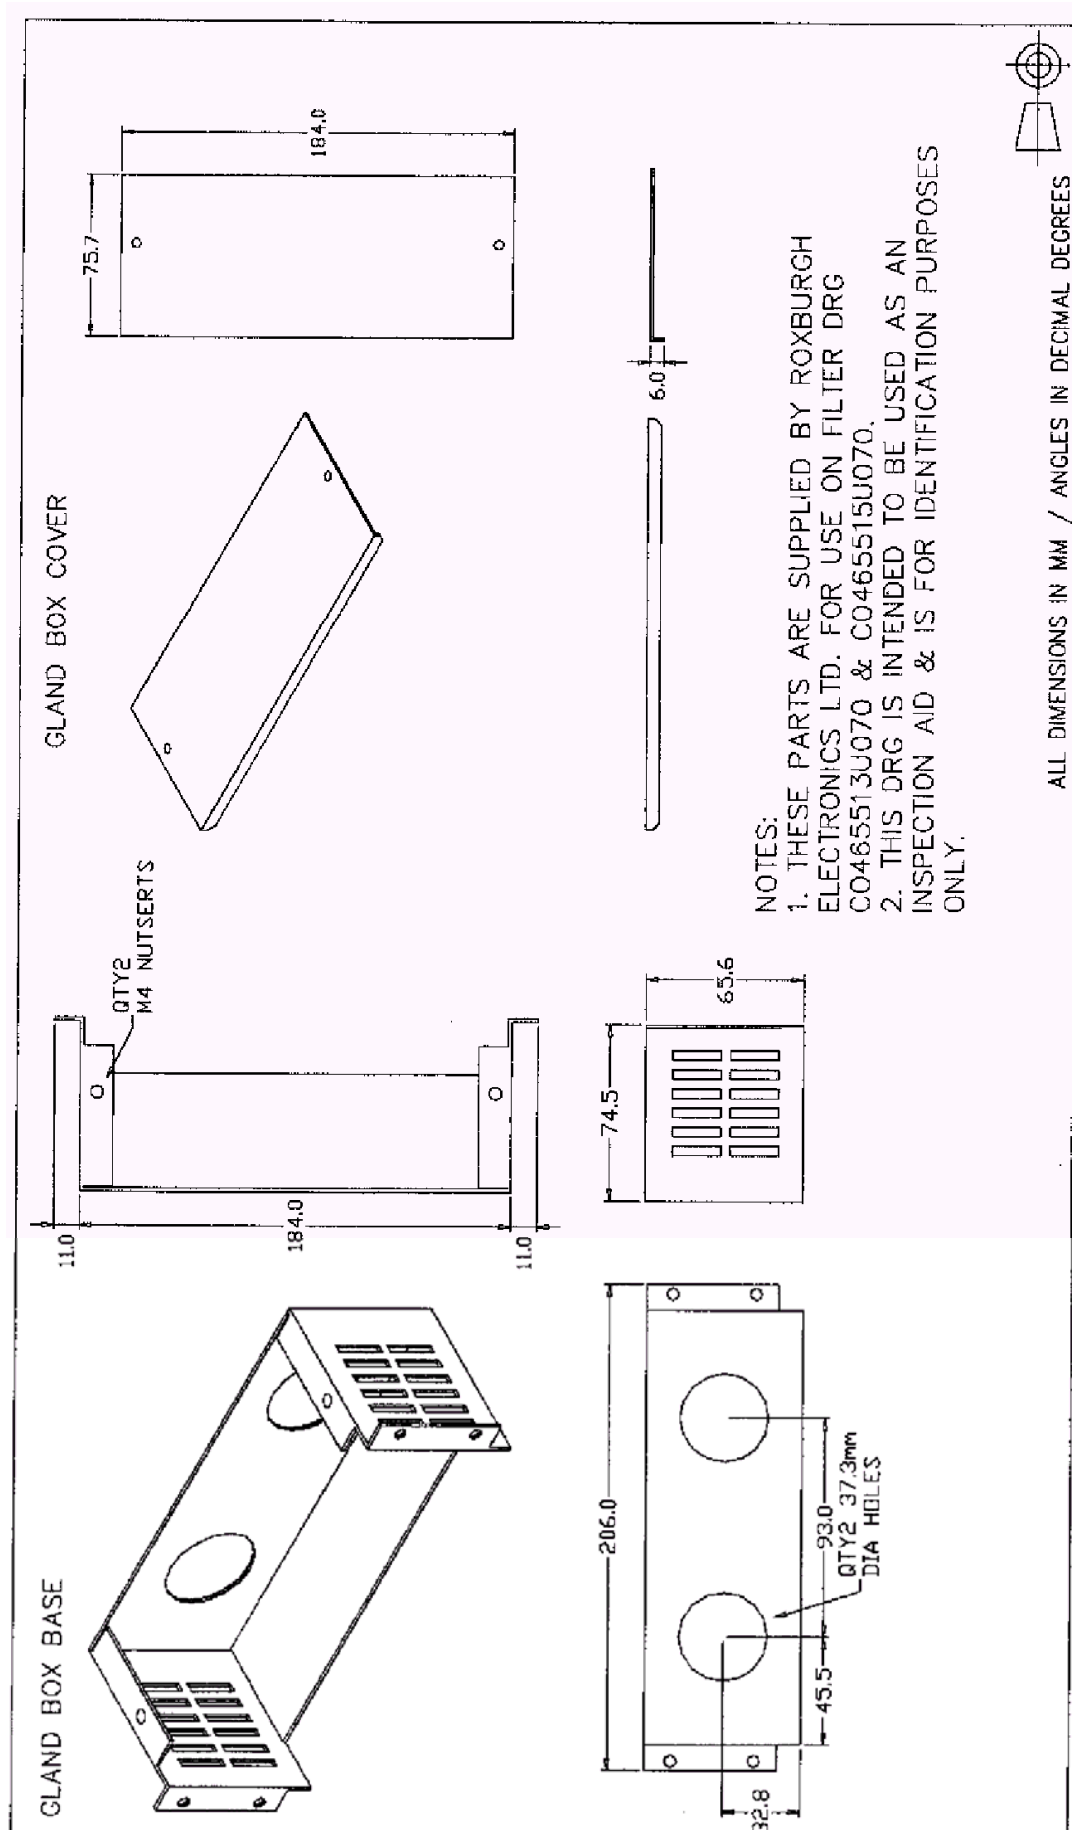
Footprint/Bookcase Mounting Filters (generic drawing)
